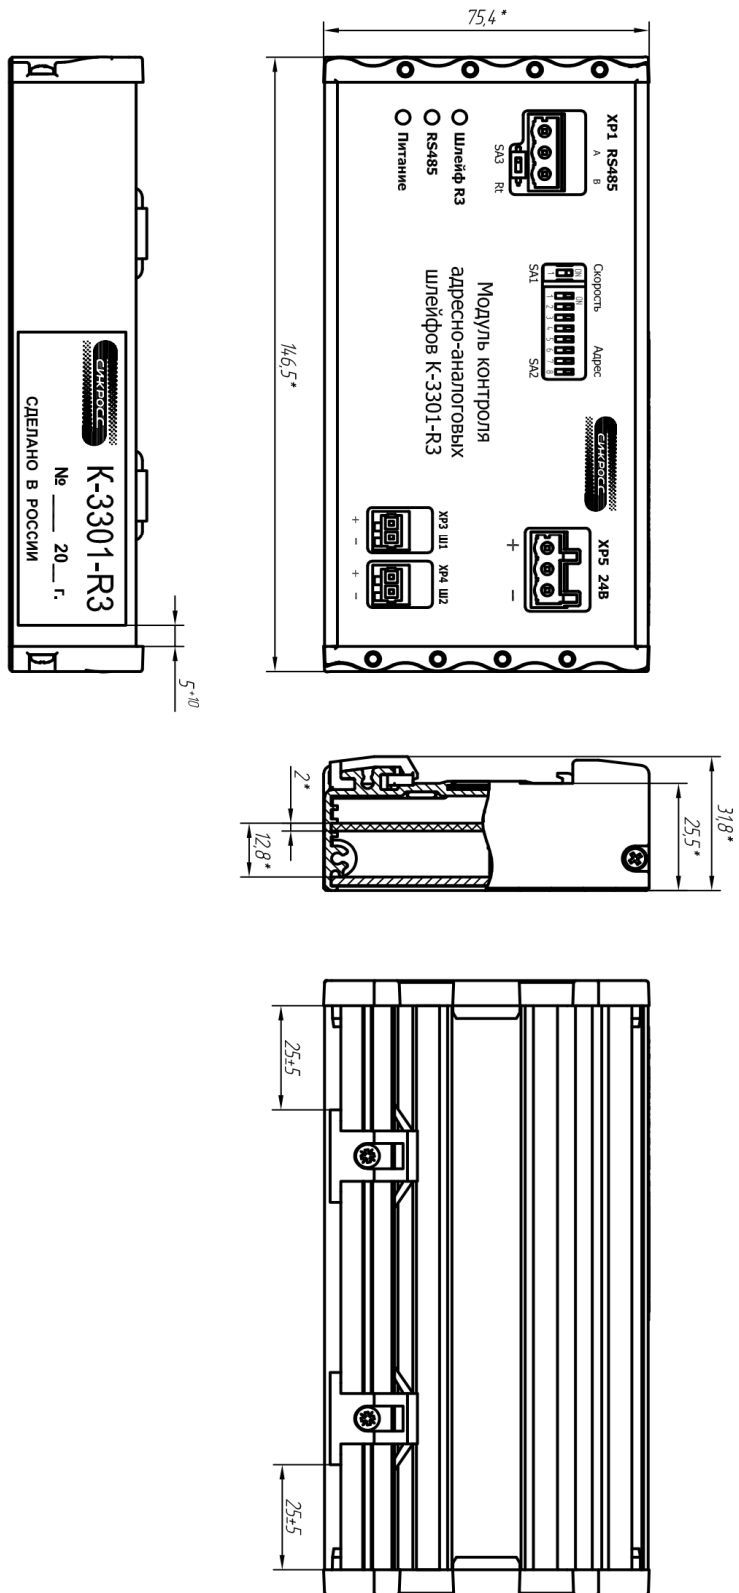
Сборочный чертеж модуля К-3301-Р3
